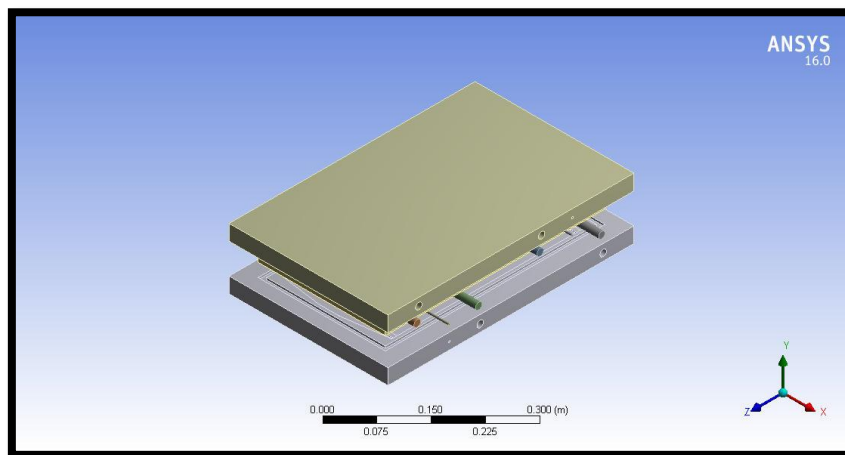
Vista isométrica con proyección de elementos de molde para espécimen.
